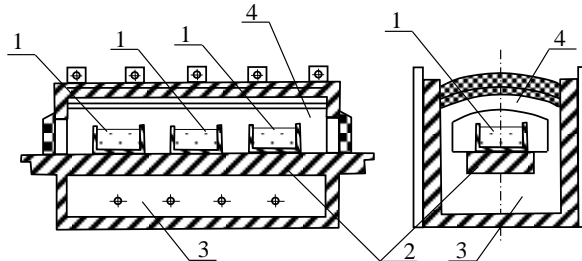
Схема топливной садочной печи: 1 – садка; 2 – под; 3 – подподовое пространство; 4 – рабочая зона печи.
